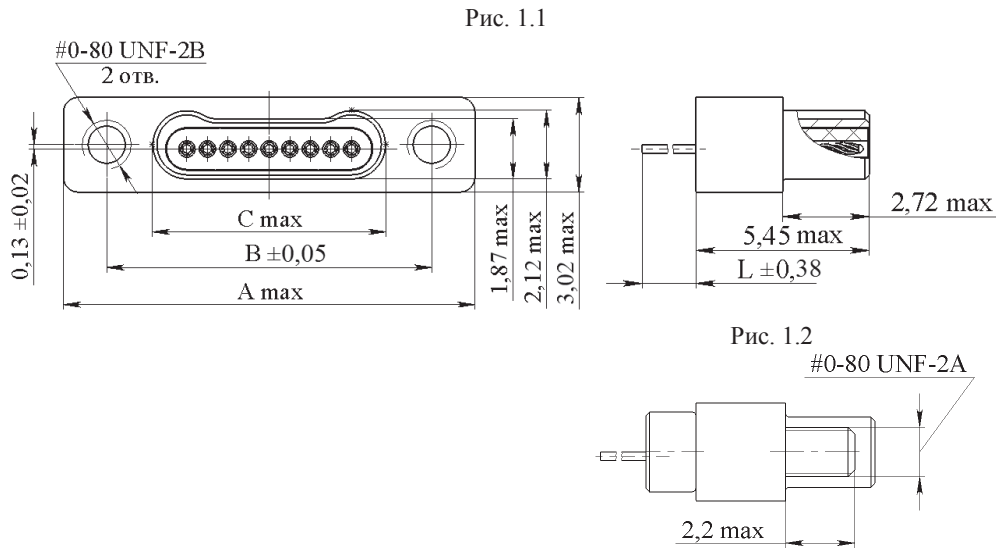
Соединитель СП450-01...1...Ш1...
